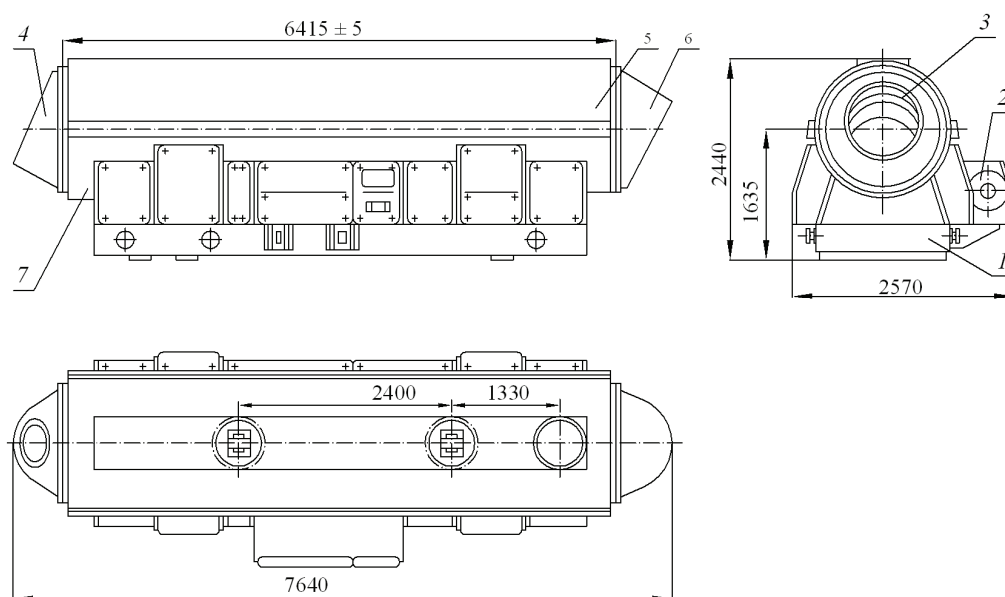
Общий вид галтовочного барабана модели 41212: 1 – рама; 2 – привод; 3 – барабан; 4 – конус передний; 5 – кожух верхний; 6 – конус задний; 7 – кожух нижний
